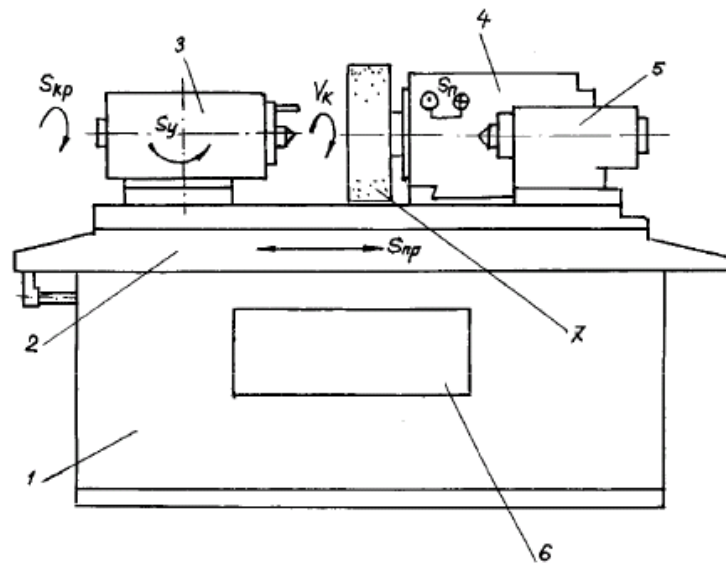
Круглошліфувальний верстат: 1 – станина; 2 – стіл; 3 – передня бабка з коробкою швидкостей; 4 – шліфувальна бабка; 5 – задня бабка; 6 – привод стола; 7 – абразивний круг.
